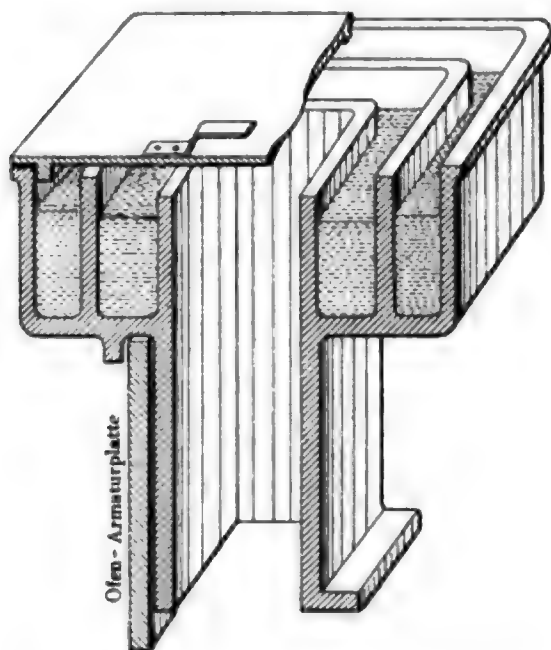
Wasserkasten mit Verschlussdeckel.
